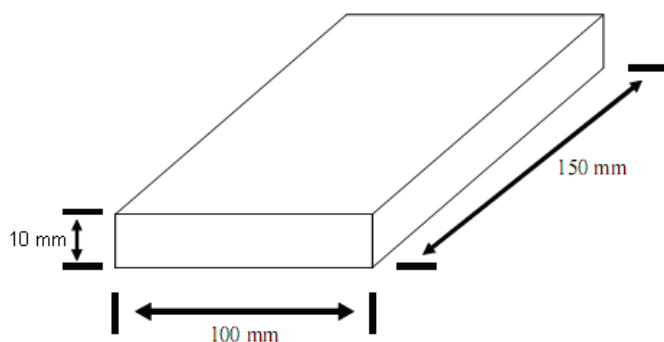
Dimensiones de las planchas para material base. Fuente: ANSI/AWS B4.0-98
